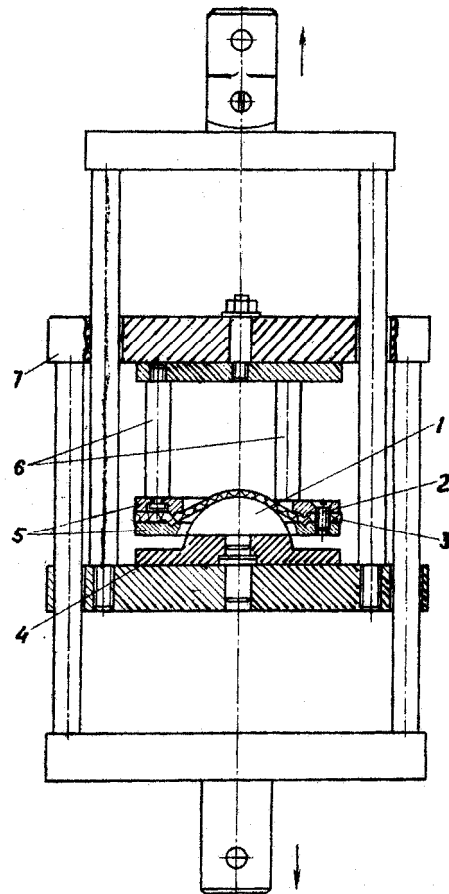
Конструктивная схема приспособления для двухосного растяжения: 1 – сферический сегмент, 2 – винты, 3 – образец, 4 – основание, 5 – обойма, 6– стойки
